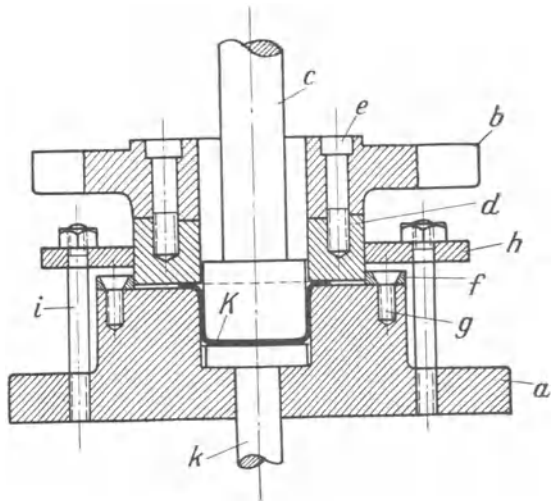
Ziehvorrichtung mit Schnitttring für Gefäße.
